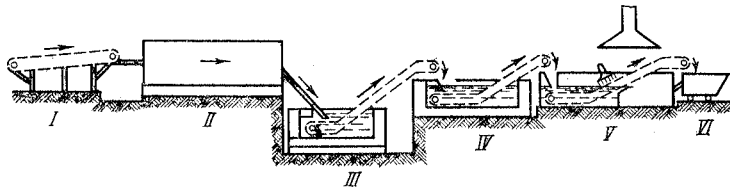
Схема непрерывной передачи деталей по конвейеру:
